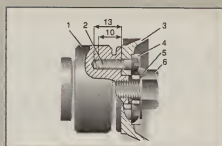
Измененная конструкция соединения распределительного вала и звездочки: 1 — распределитель; 2 — винт М6; 3 — звездочка; 4 — опорная шайба; 5 — контрольная шайба; 6 — центральный болт.
